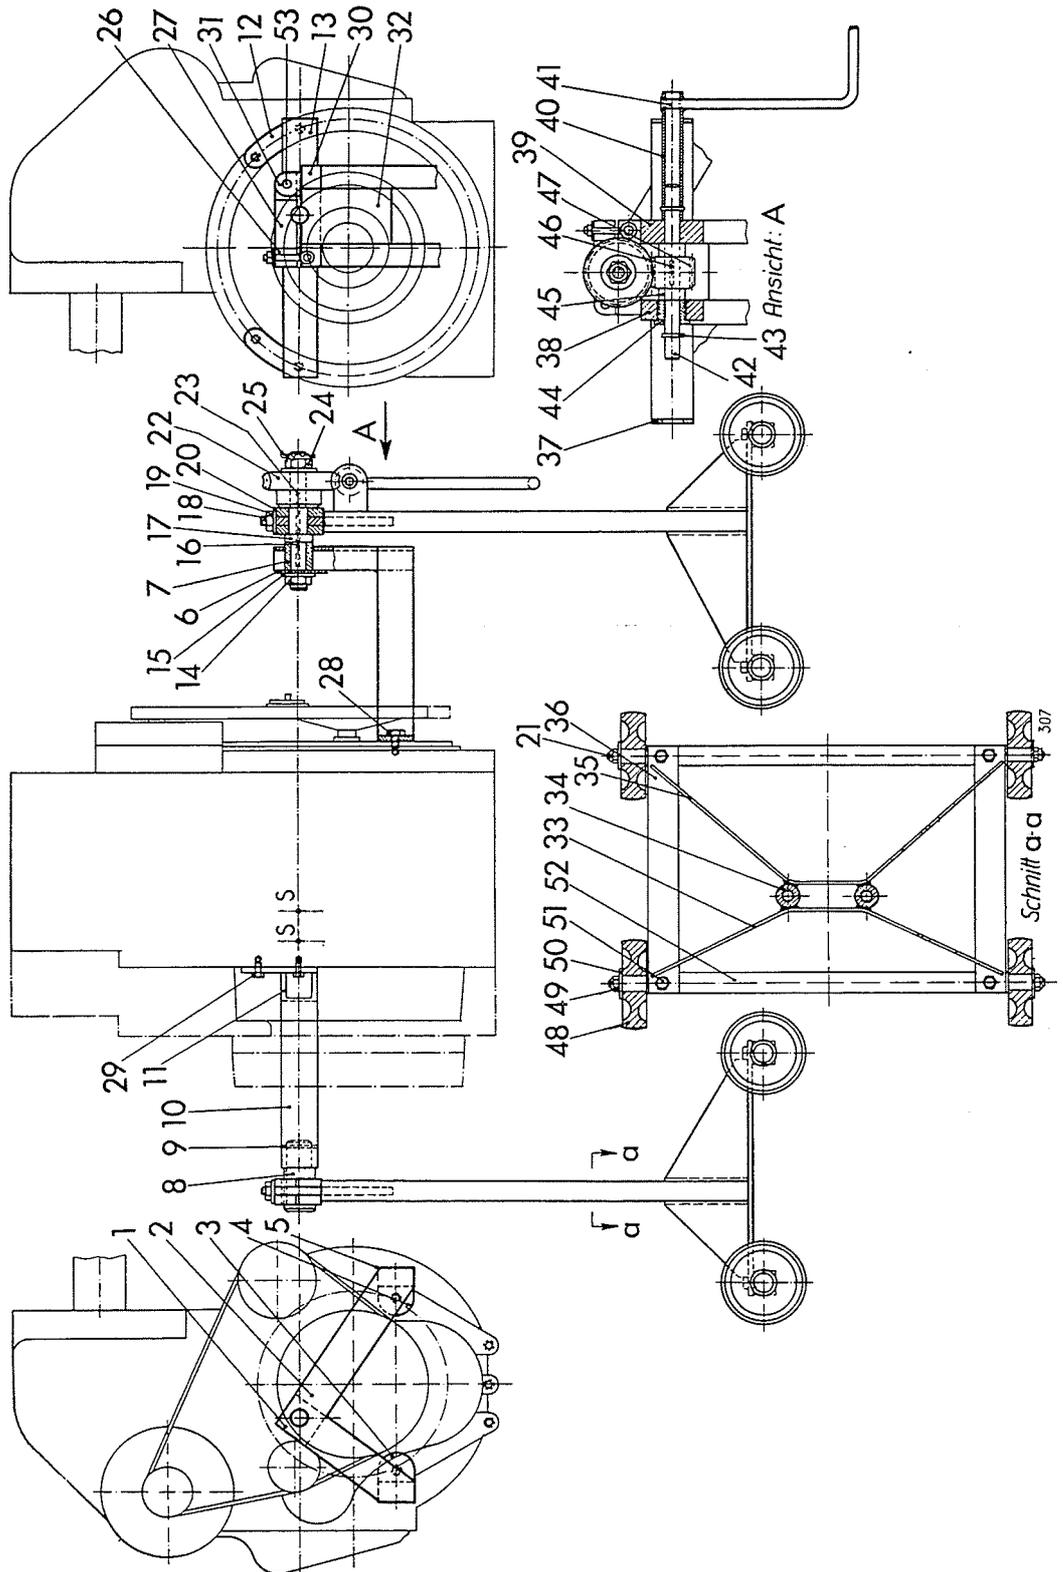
Montagebock für Motoren, mit Aufnahmeteilen für F/A 2-3L 514 gezeichnet (Hierzu Bilder Nr. 308, 309, 310 und Angaben zum Montagebock)
